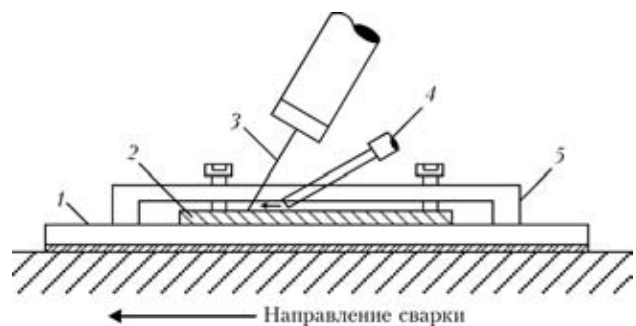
Схема процесса лазерной сварки: 1 — оснастка для сборки сварки; 2 — свариваемый образец; 3 — лазерный луч; 4 — сопло для защитного газа; 5 — зажимное приспособление
